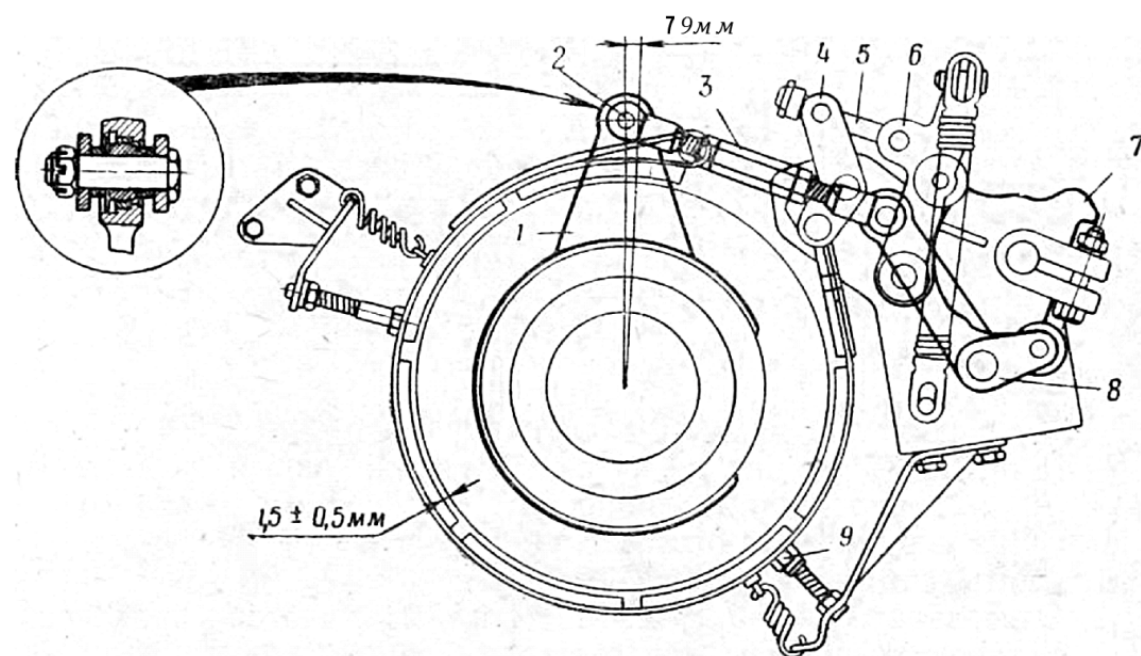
Схема регулировки свободного хода поводковой коробки фрикциона механизма поворота:
